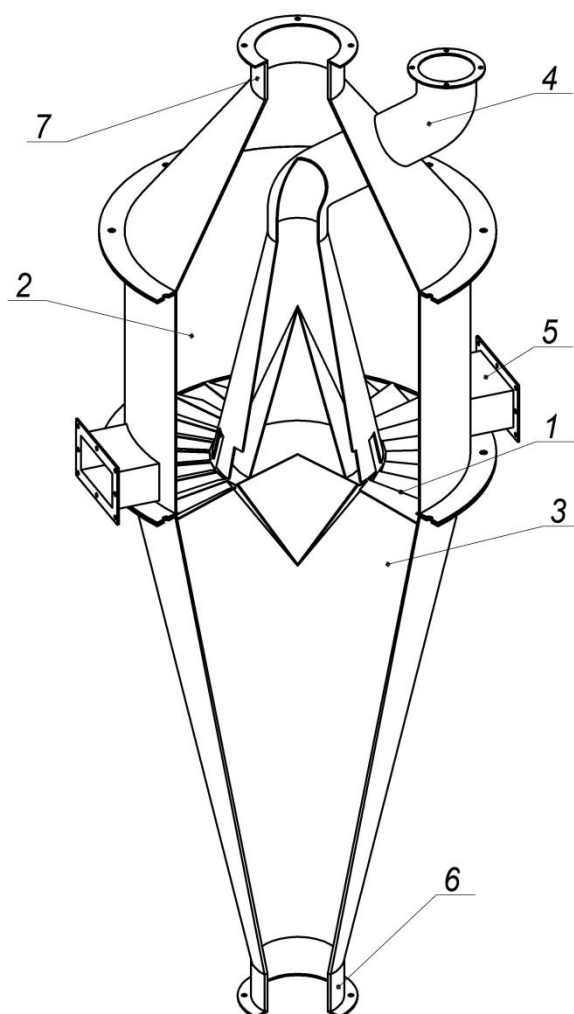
Схема сушильной установки: 1 – решетка газораспределительная; 2 – рабочая камера; 3 – газовая камера; 4 – загрузочный патрубок; 5 – разгрузочный патрубок; 6 – газоподводящий патрубок; 7 – газоотводящий патрубок
